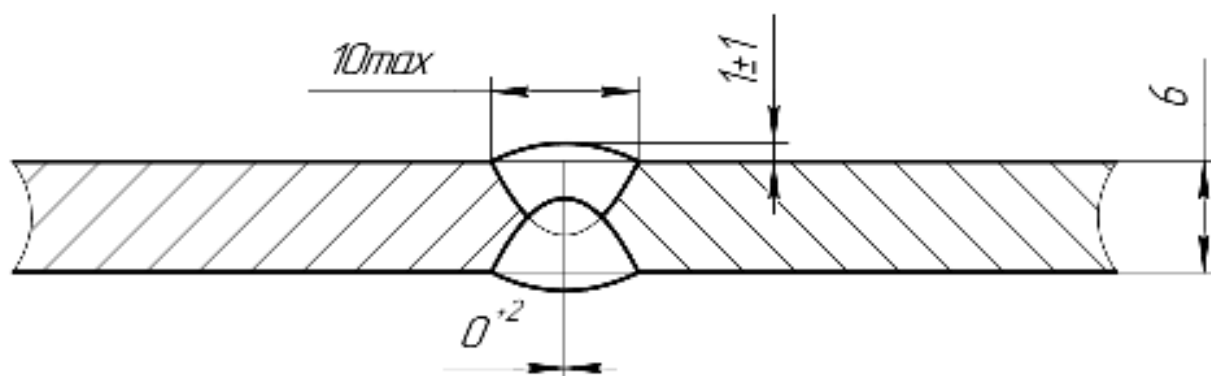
Конструктивные элементы сварного шва С7 ГОСТ 14771-76
